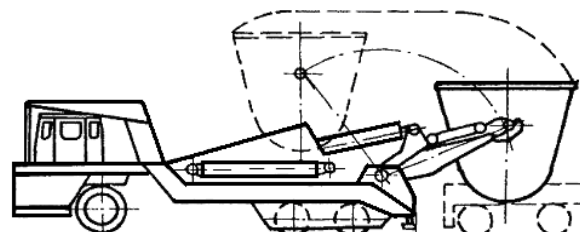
Автошлаковоз. Схема перестановки заполненной шлаковой чаши
